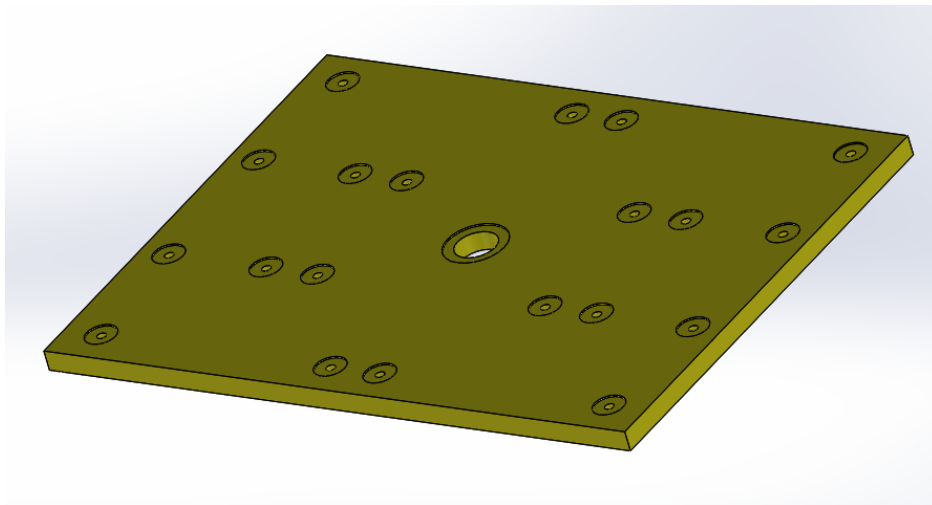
Placa tapa, parte del ensamblaje del molde.
